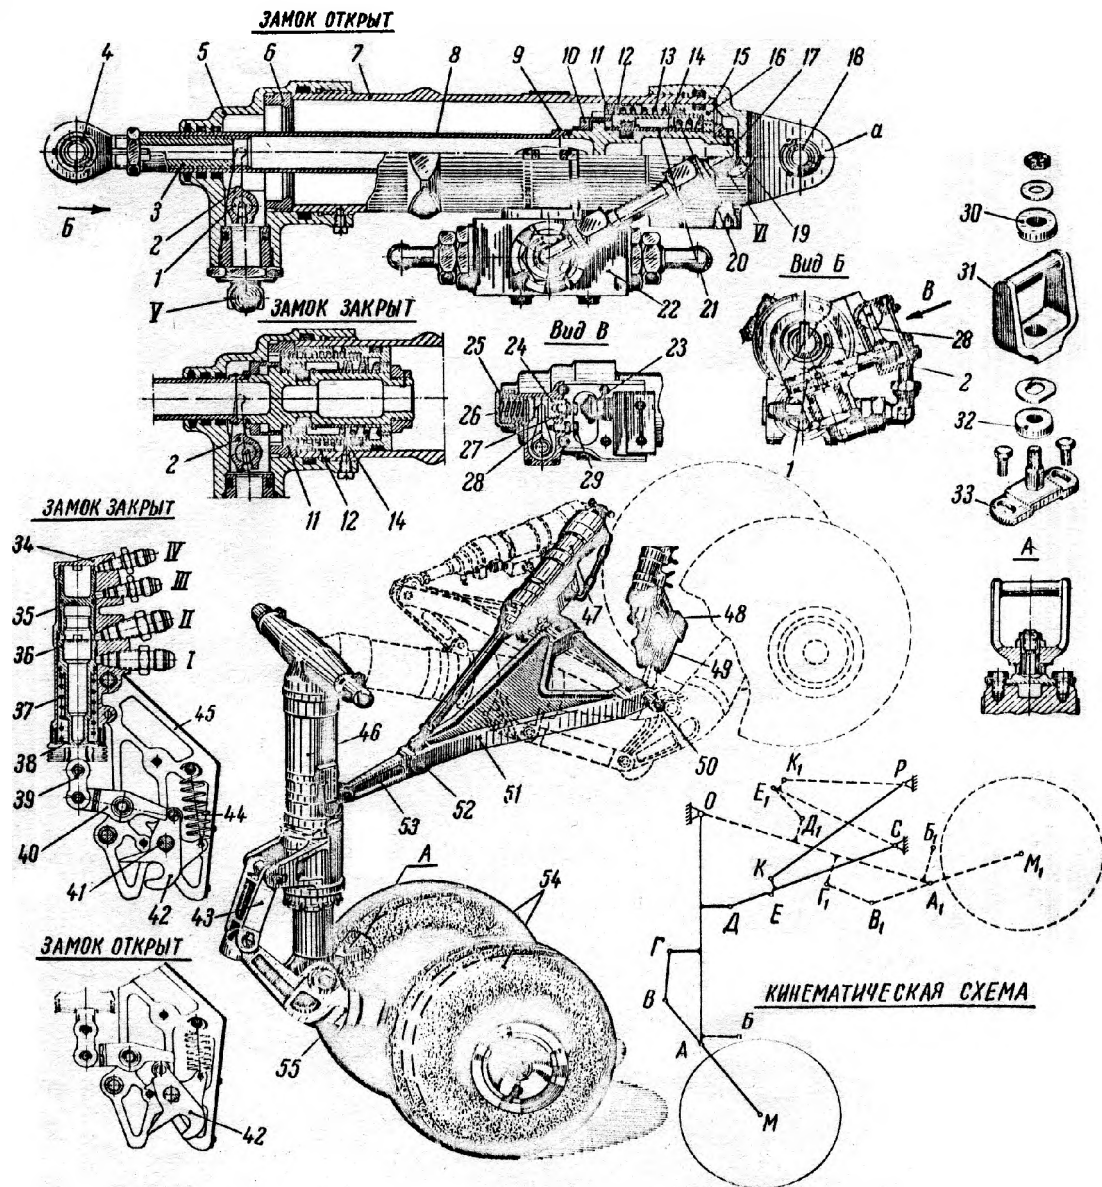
Передняя стойка шасси с механизмом уборки и выпуска вертолета Ми-24А [13]:
